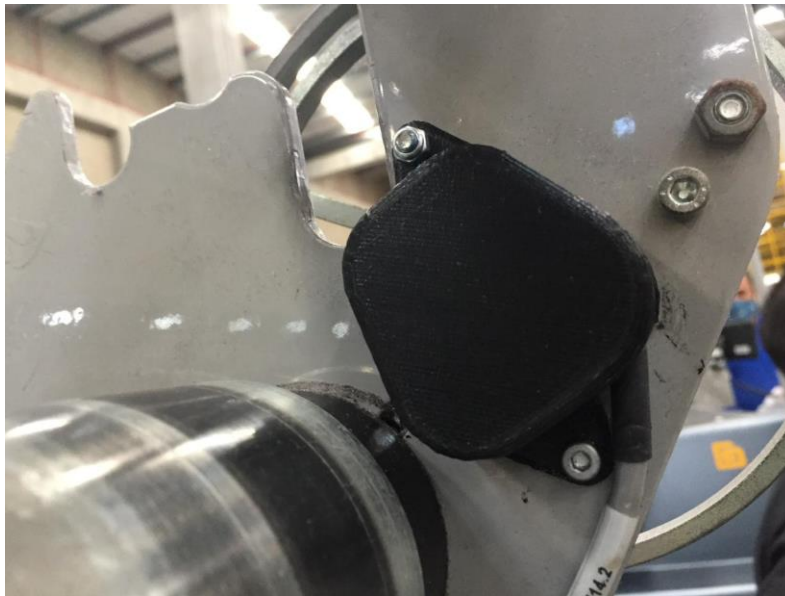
, Pieza final montada en máquina, tomada de fuente propia.
